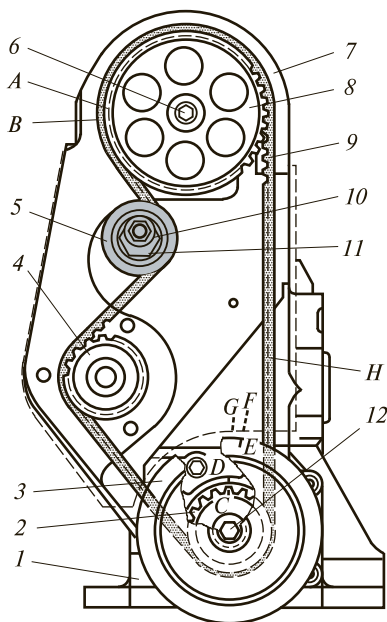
Схема привода механизма газораспределителя автомобиля ВАЗ-2108:
